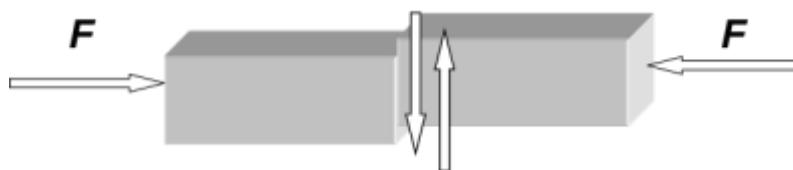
Схема линейной сварки трением (ЛСТ)
